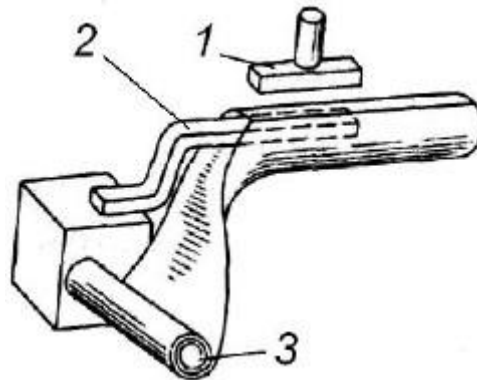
Схема сварки рукавов из пленки продольным швом: 1 – верхний электрод; 2 – нижний электрод; 3 – рулонный материал Сварка ТВЧ может быть использована и для изготовления объемных изделий, для чего служат электроды сложной формы.
